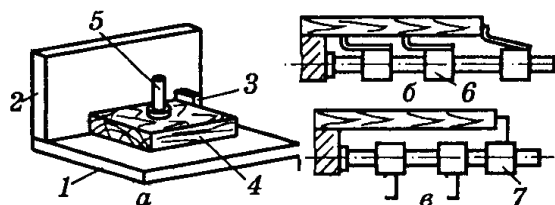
Базування заготовок призматичної форми з упорами: а – нерухомими; б – пружними; в – відкидними: 1 – стіл; 2 – напрямна лінійка; 3 – упор; 4 – заготовка; 5 – затискач; 6 – пружні упори; 7 – відкидні упори
